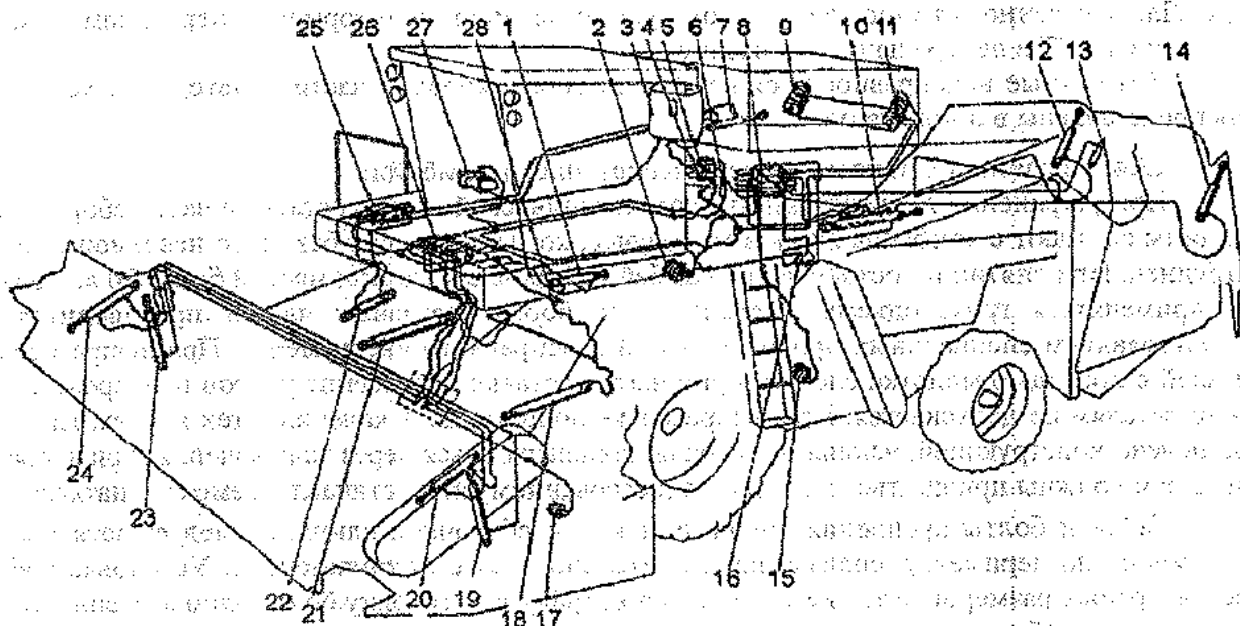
Схема основной гидросистемы комбайна «Дон»: 1-гидроцилиндр включения молотилки ГА-93.000-10; 2-гидроцилиндр вариатора барабана РСМ-10.09.01.010А-03; 3- гидробак РСМ-10Б.09.09.360 (двигатель СМД-31А) или РСМ-10Б.09.69.010А (двигатели ЯМЗ-238АК и 740.12.-210 КАМАЗ) или РСМ-10Б.09.69.010А-01 (двигатель Д-461-51АМЗ); 4-полумуфта наружная Н036.67.100-10; 5-клапан напорный КН50.12,5; 6-гидроклапан с электромагнитным управлением КЭ1,6-2,5-16-01; 7-гидроцилиндр включения выгрузного шнека ГА-93.000-06; 8-элект-рогидрораспределитель 4РЭ50-29; 9, 11-вибраторы ГА-40.000В; 10-гидроцилиндр поворота выгрузного шнека ГЦ 63.500.16.000; 12, 14-гидроцилиндр закрытия копнителя 54-9-145-06; 13-гидроцилиндр открытия защелки копнителя ГА 66.010А-03; 15-гидроцилиндр вариатора вентилятора очистки ЦС 83.000 А; 16-распределитель копнителя РК 00.000-06; 17-гидроцилиндр вариатора мотовила ГА-83. 000А; 18, 21-гидроцилиндр подъема жатки РСМ-10.09.02.100Б; 19-гидроцилиндр вертикального перемещения мотовила ГА-81.000-08; 20-гидроцилиндр горизонтального перемещения мотовила ГЦС 32.180.16. 000А или ЦГС 32.16.000-02; 22-гадроцилиндр прокрутки жатки ГА 93.000-08; 23- гидроцилиндр вертикального перемещения мотовила ГА-80.000-03; 24-гидроцилиндр горизонтально-го перемещения мотовила ГЦ 40.180.16. 000А или ЦГ 40.16.000-02; 25- электрогидрораспределитель 2РЭ50-00; 26-электрогидрораспределитель 5РЭ50-44; 27-насос НШ-32А-3 (двигатель СМД-31А) или НШ-32М-4 (двигатель ЯМЗ-238АК) или НШ-32А-3-Л (двигатель Д461-51АМЗ) или НШ32У-3 (двигатель 740.12-210 КАМАЗ); 28-клапан дросселирующий настраиваемый КДН 00.000-06.
